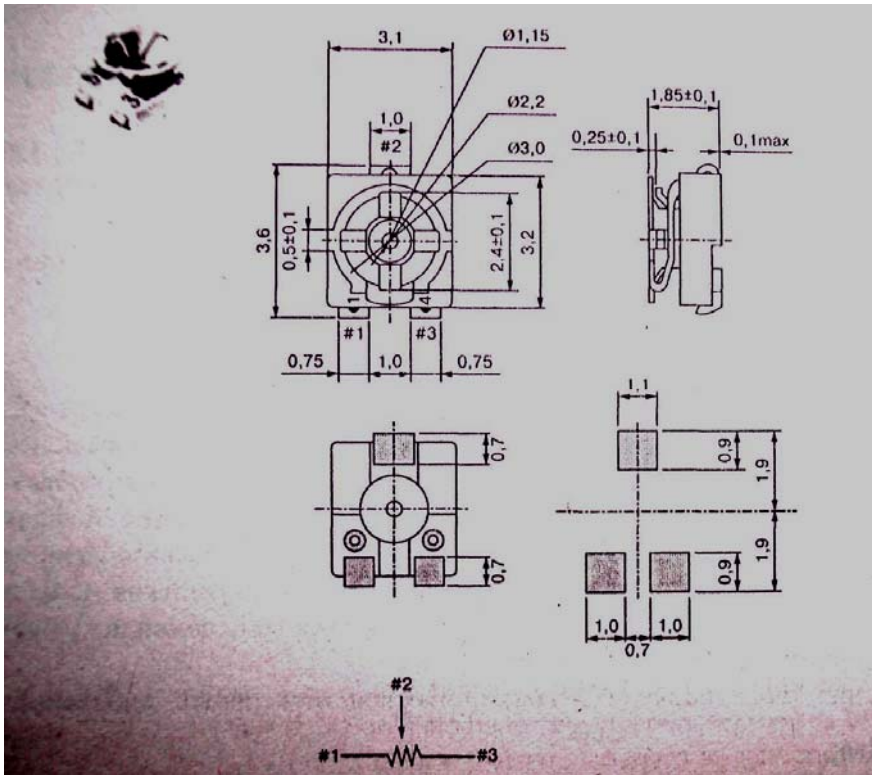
Общий вид, конструкция, габаритные и присоединительные размеры подстроечного углеродистого резистора серии POZZAN
